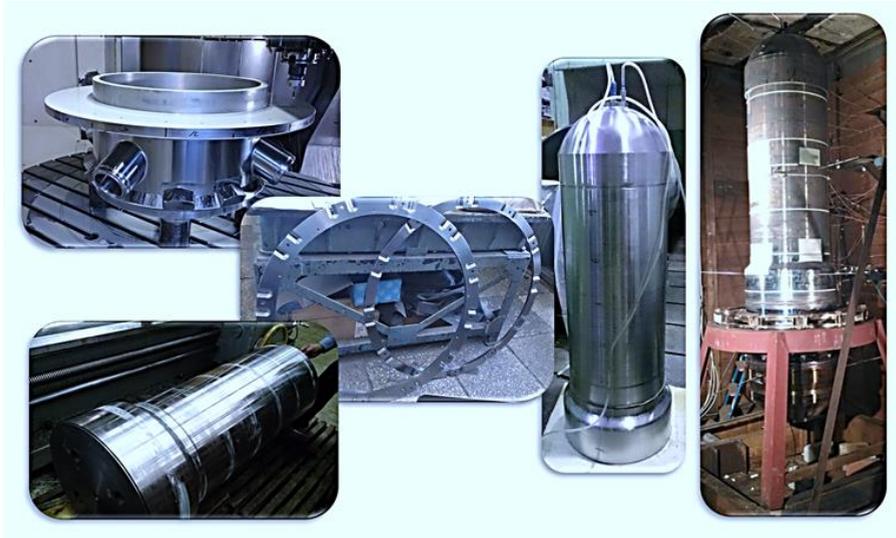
Полномасштабный макет корпуса реактора для термоциклических и пневматических испытаний
